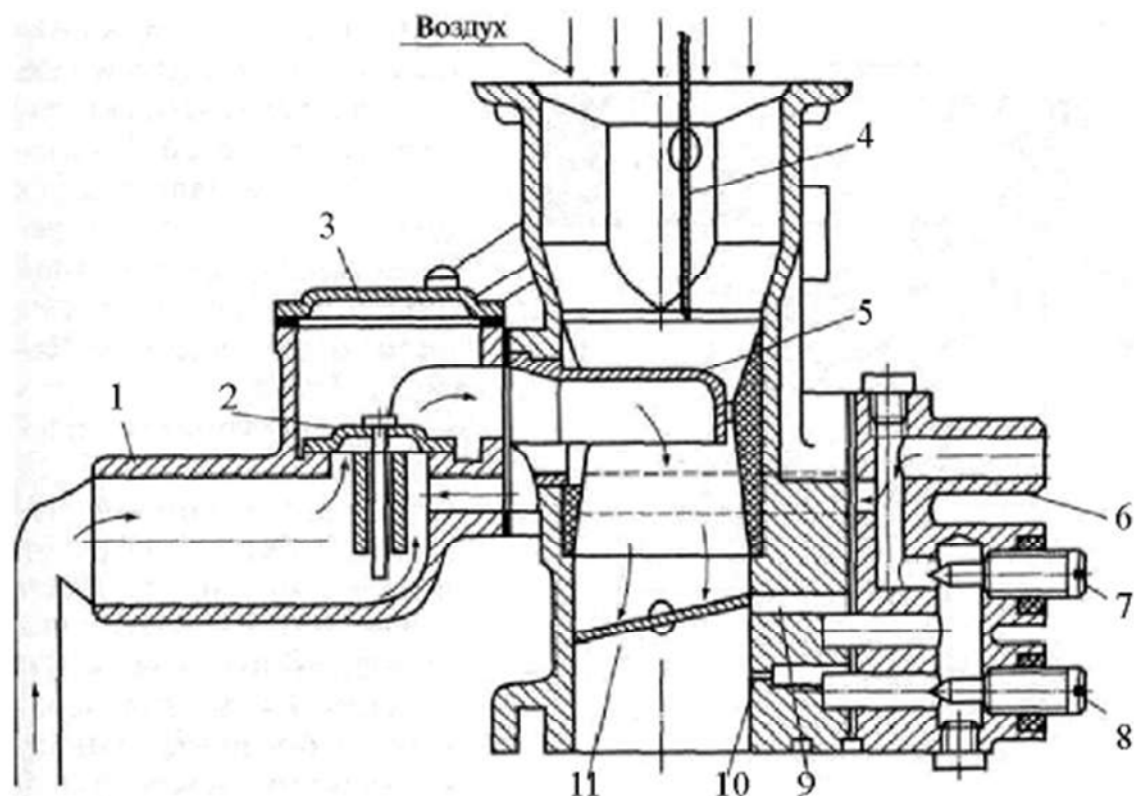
Смеситель СГ-250: 1 и 6 - патрубки подвода газа; 2 - обратный клапан; 3 - крышка; 4 - воздушная заслонка; 5- газонаполнительное устройство; 7- регулировочный винт переходных режимов; 8 - регулировочный винт системы холостого хода; 9 - канал холостого хода; 10 - канал переходного режима; 11 - дроссельная заслонка.
